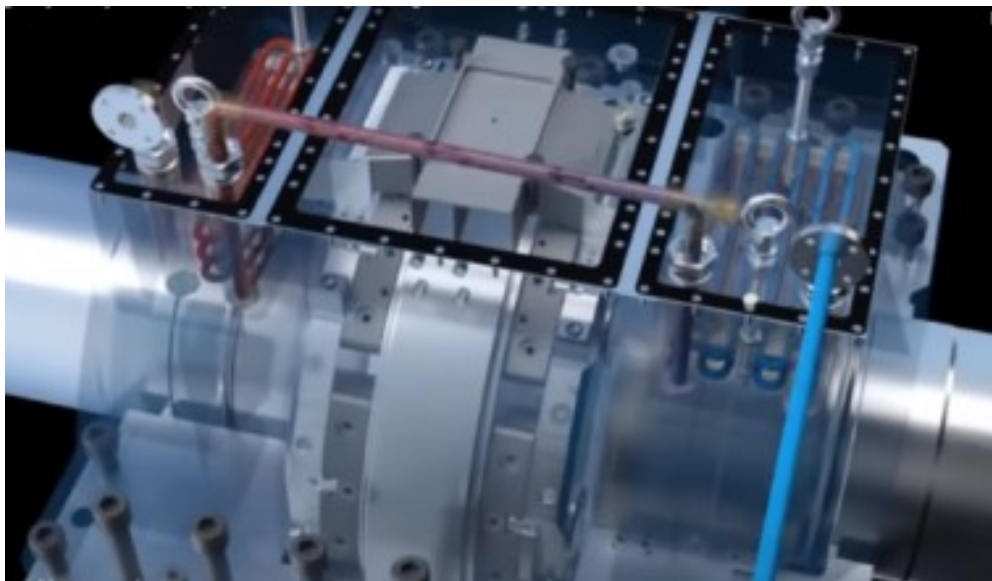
Εξοπλισμός αυτοματισμού και ένδειξης θερμοκρασίας [*Michell Bearings hydrodynamic propeller shaft bearing and thrust block - YouTube*]
